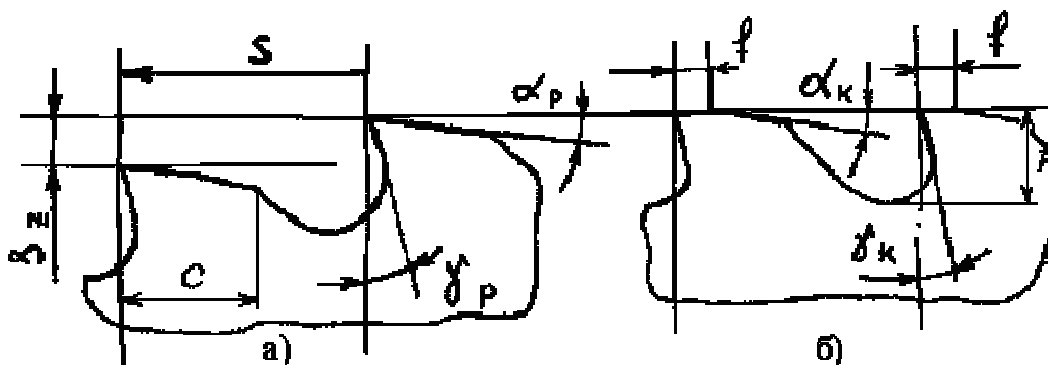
Профиль: а) режущих и б) калибрующих зубьев протяжки.
